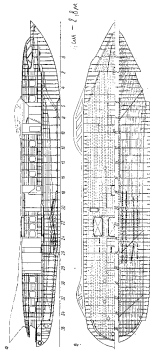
Конструктивная схема корпуса теплохода «Варяг»: а — продольный разрез; б — план палубы и днища
